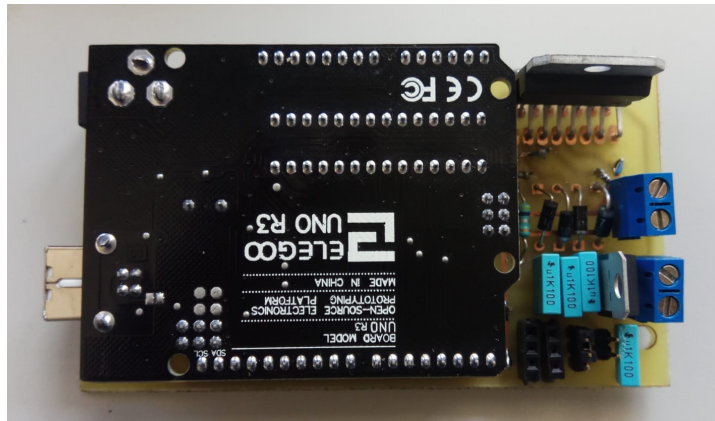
Etapa de construcción y soldadura de la PCB con el driver implementado
